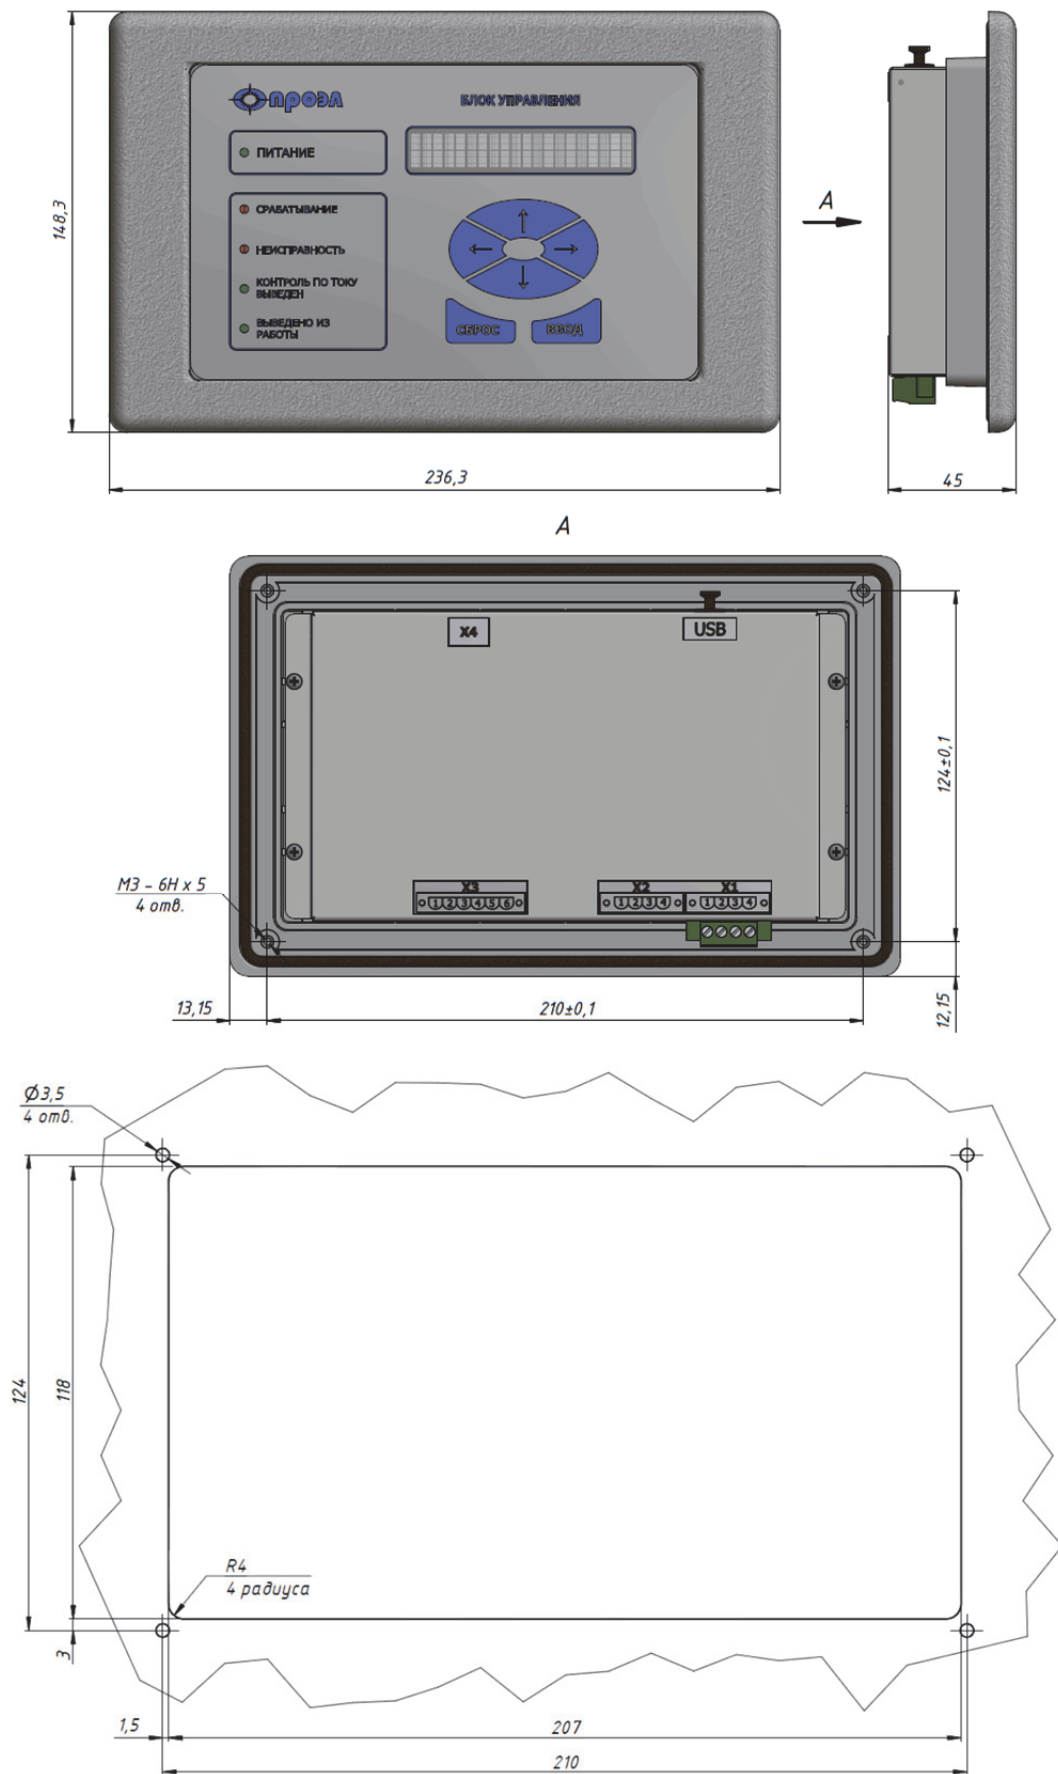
Габаритный чертеж БУП и чертеж разметки для доработки панели.
